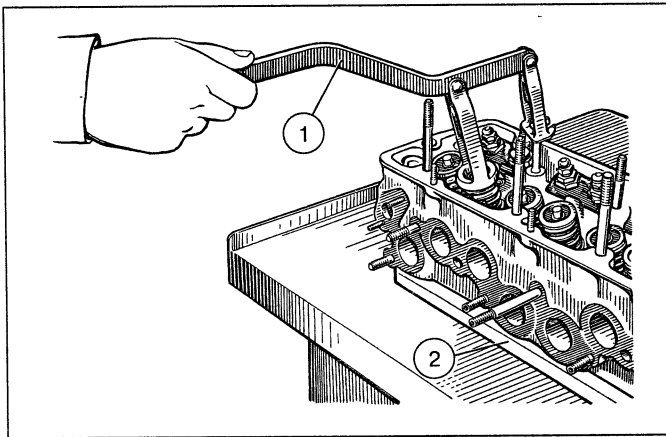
Снятие пружин клапанов: 1 – приспособление А.60311/R; 2 – подставка
